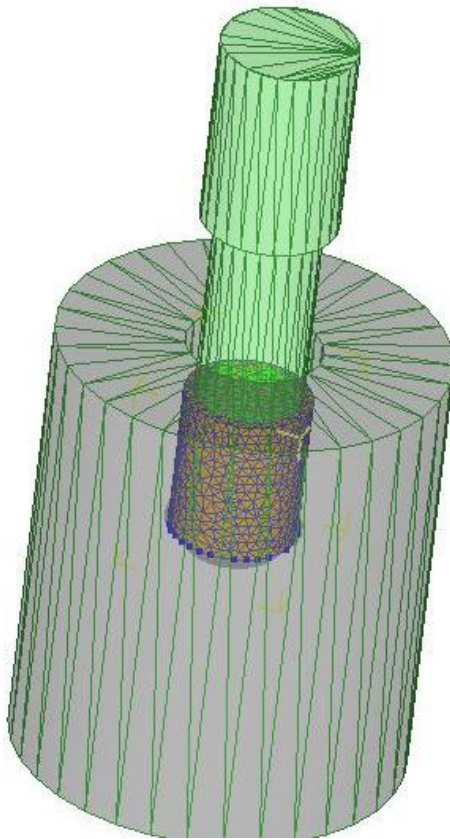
Розрахункова схема системи матриця - заготовка - пуансон.
